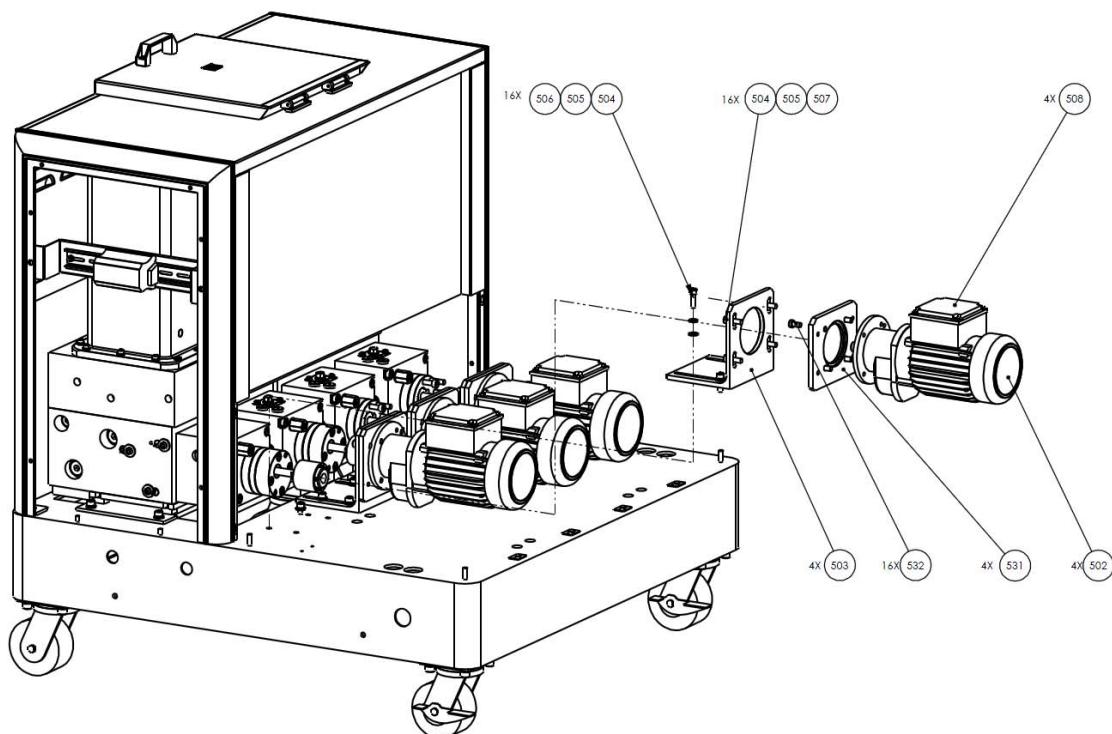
Peças do conjunto do motor (está ilustrado o aparelho de fusão com 4 bombas)
